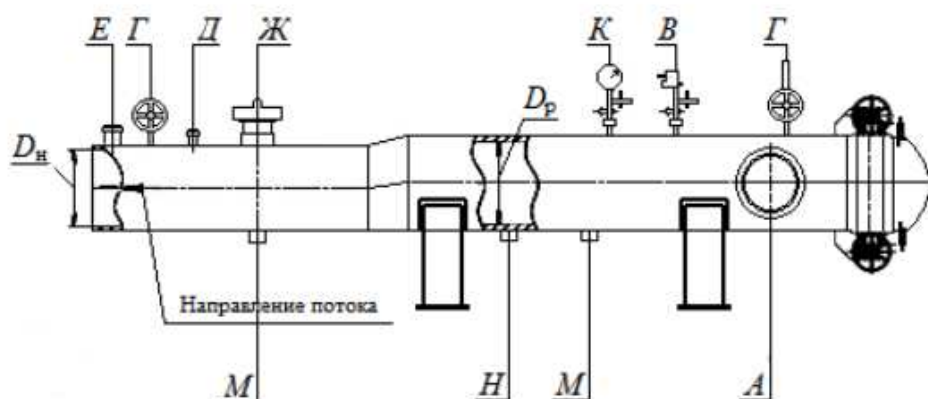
Камера запуска СОД: А – патрубок подвода потока; В – патрубок для датчика давления; Г – патрубки для присоединения трубопроводов газовой воздушной линии; Д – патрубок для подачи пара или инертного газа; Е – патрубок для установки сигнализатора рычажного; Ж – патрубок для установки запасочного устройства; К – патрубок для установки манометра; М – патрубки для присоединения дренажных трубопроводов; Н – датчик контроля герметичности
